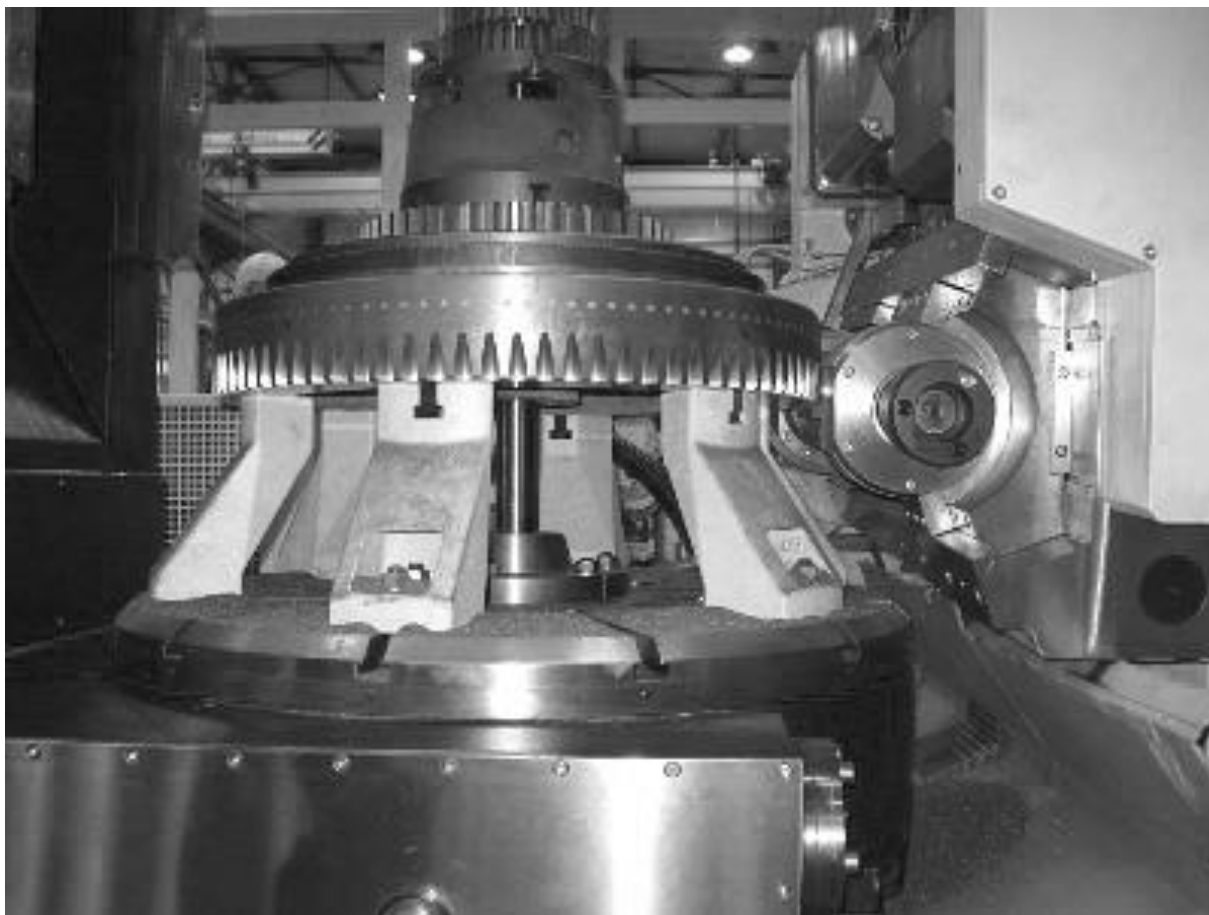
Вертикальный копировальный зубофрезерный станок
